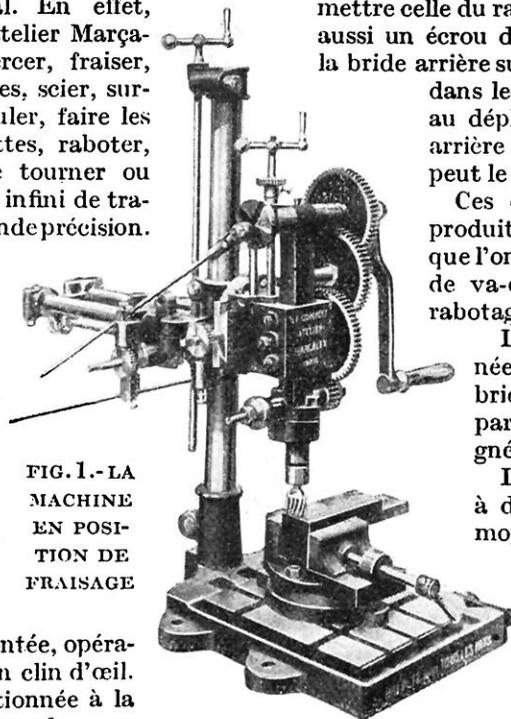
LA MACHINE EN POSITION DE FRAISAGE
